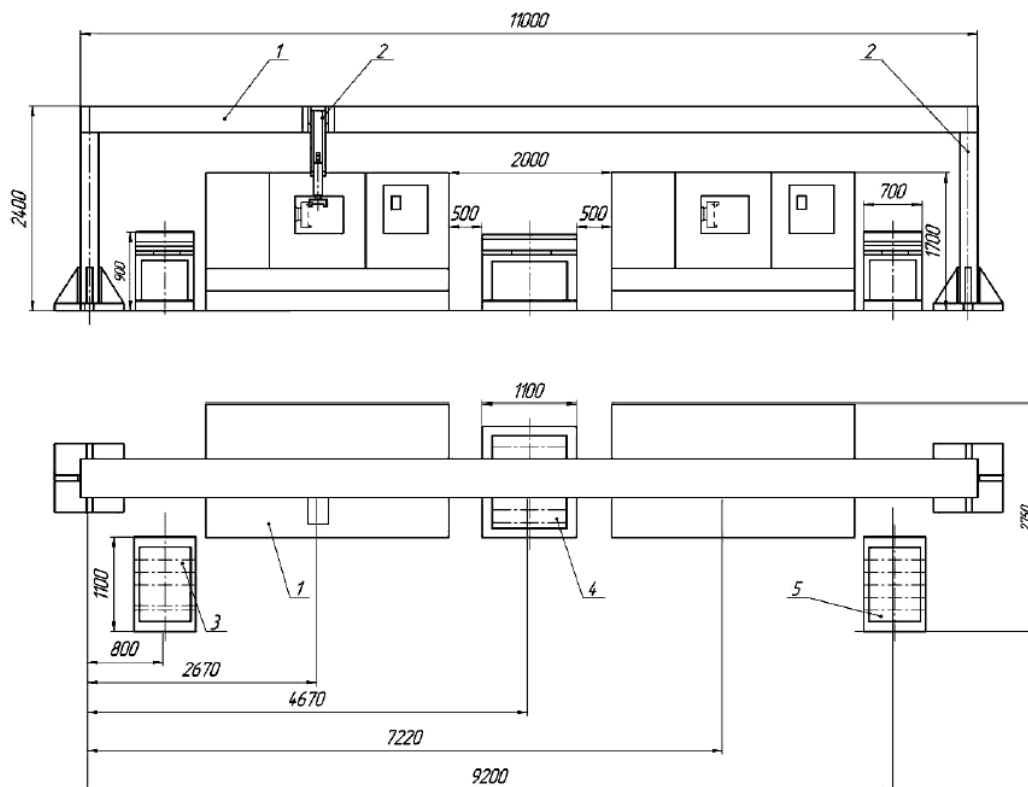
Компоновочная схема РТК на базе ПР портального типа
